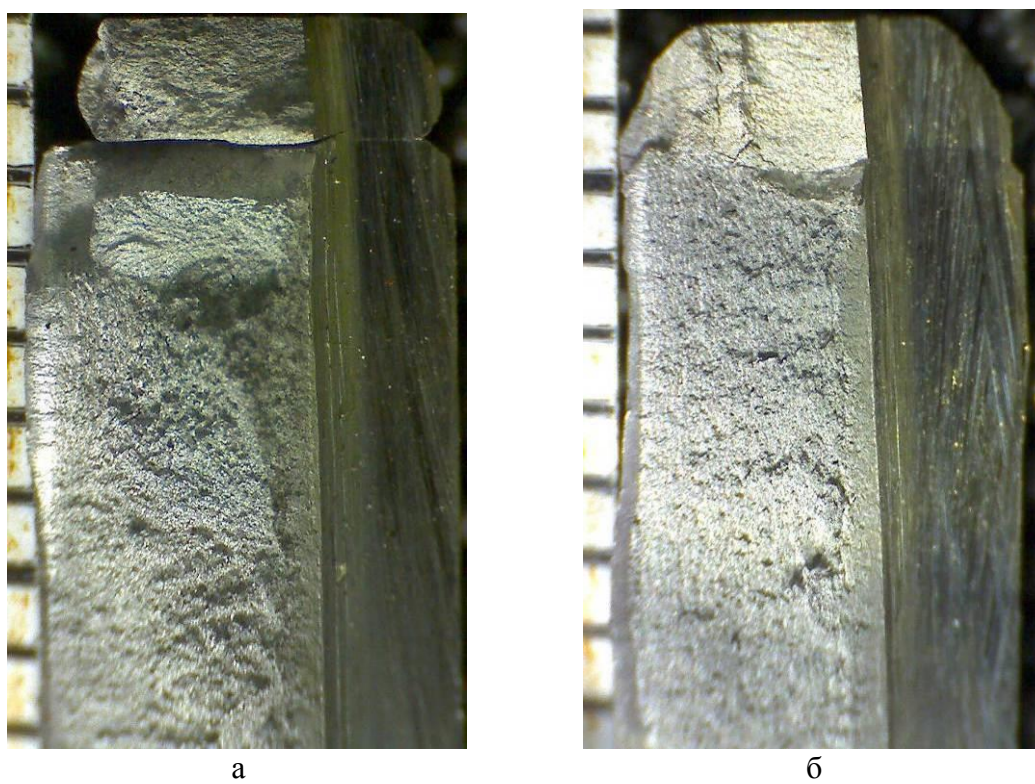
Изломы образца, наплавленного с двойным управлением переносом металла:
